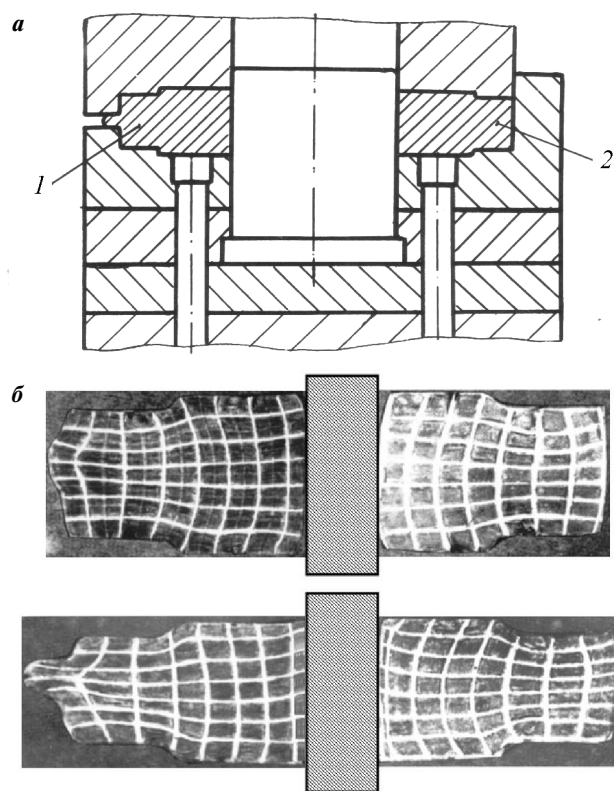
Схема штампа для горячей штамповки пористых заготовок (а) и внешний вид продольных сечений поковок с нанесенной координатной сеткой после осадки с разными степенями деформации (б)
